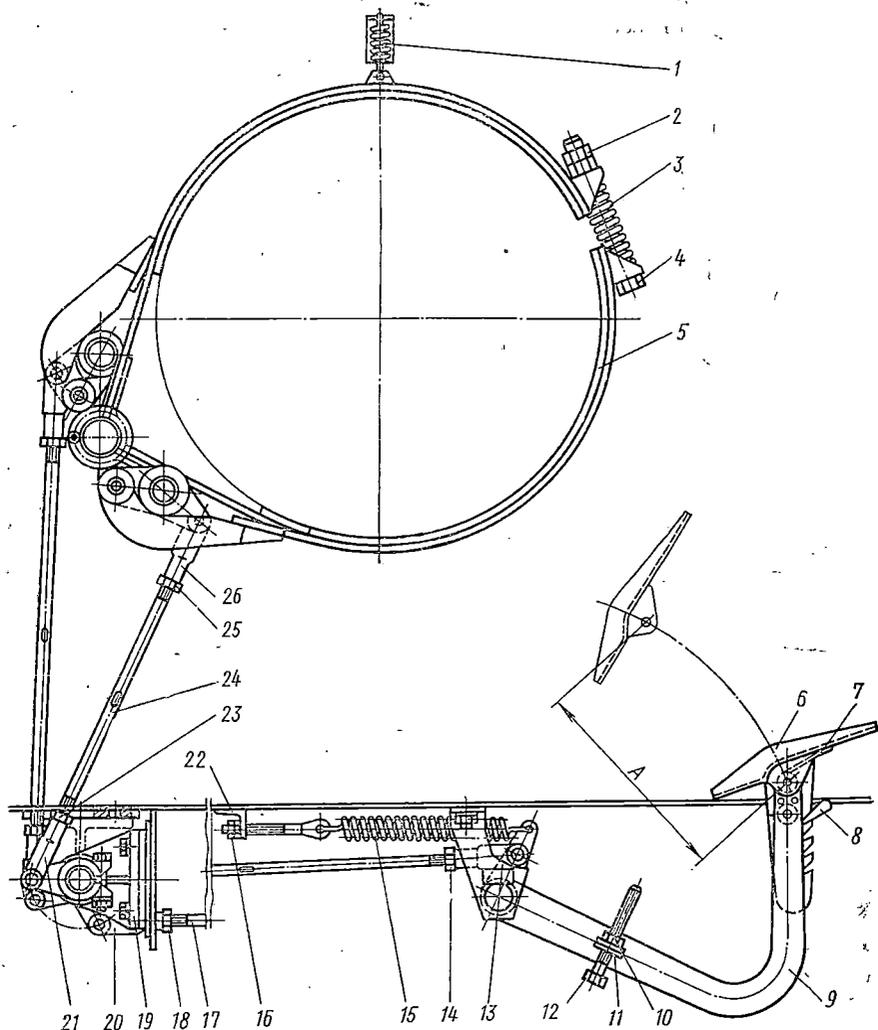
Тормоз главной лебедки экскаваторов Э-302Б и Э-304Б:
